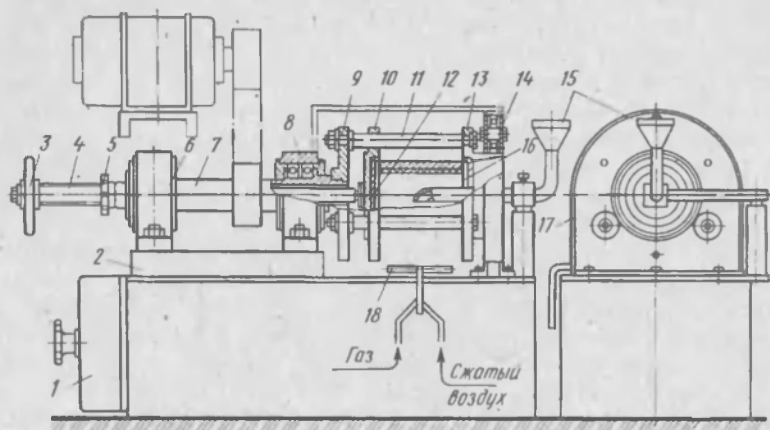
Стационарный станок для центробежной заливки баббитом подшипников скольжения
